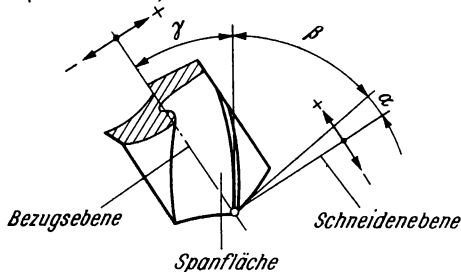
Winkel im Werkzeugbezugssystem am Spiralbohrer
